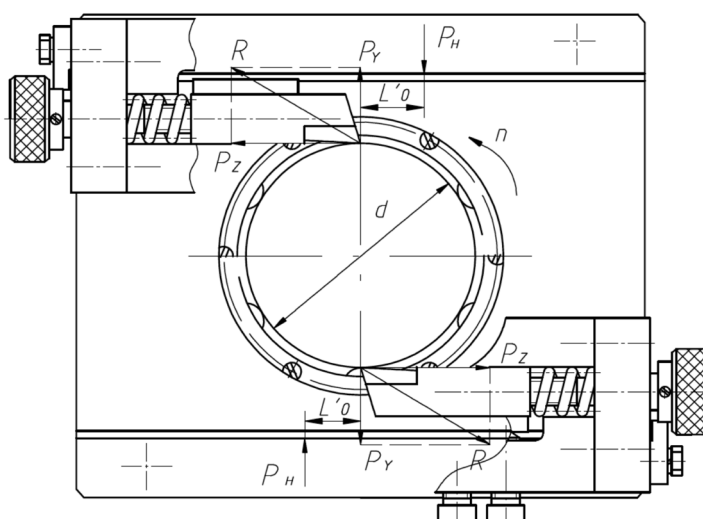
Тангенциальная установка резцов по отношению к обрабатываемому валу в резцовой головке
